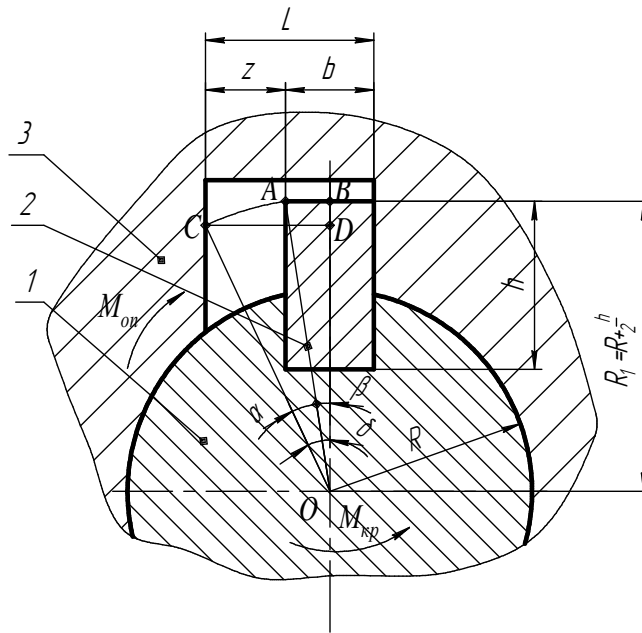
Розрахункова схема для визначення можливого значення кута повороту зірочки: 1 – вал; 2 – шпонка; 3 – зірочка
